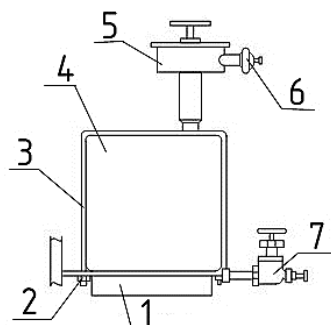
Устройство емкости под пенообразователь пожарного автомобиля: 1 – подрамники; 2 – гайка; 3 – хомут; 4 – бак; 5 – заливная горловина; 6 – рукавная головка; 7 – вентиль
